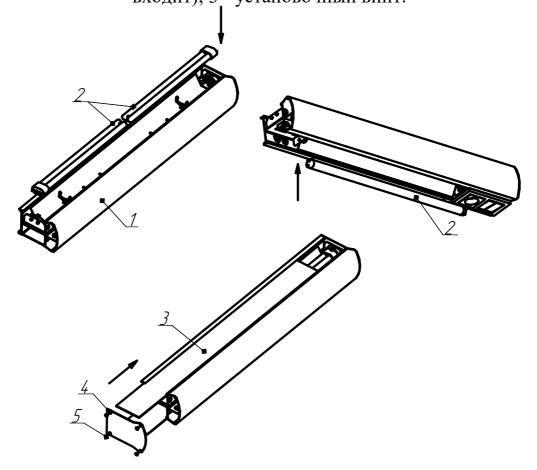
Установка ламп в светильник ЛБО58. 1 - корпус светильника; 2 - лампы; 3 - рассеиватель; 4 - торцевая крышка; 5 - винт самонарезающий.
